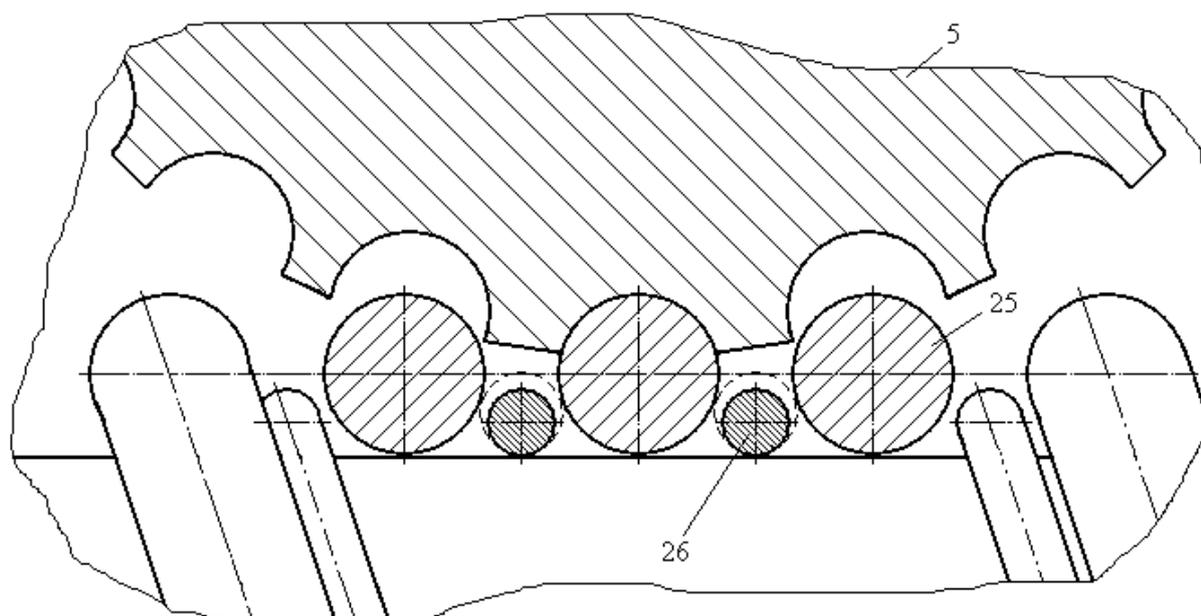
Схема привода с червяком в виде вала с охватывающими его двумя пружинами
